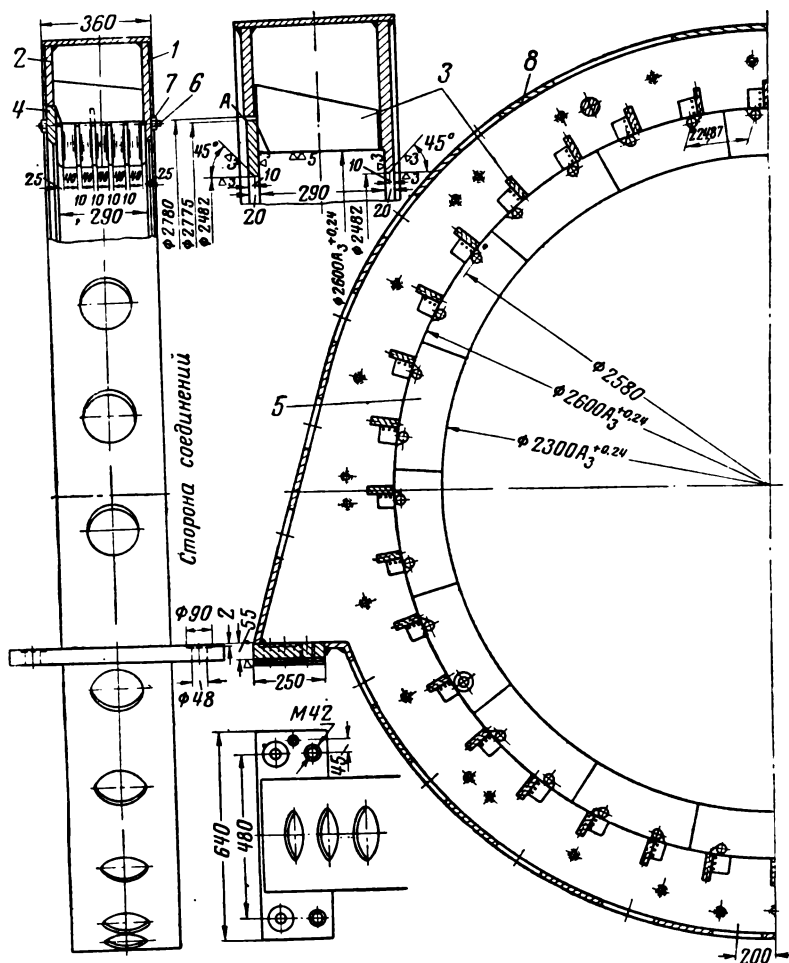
Сварная станина машины переменного тока.
